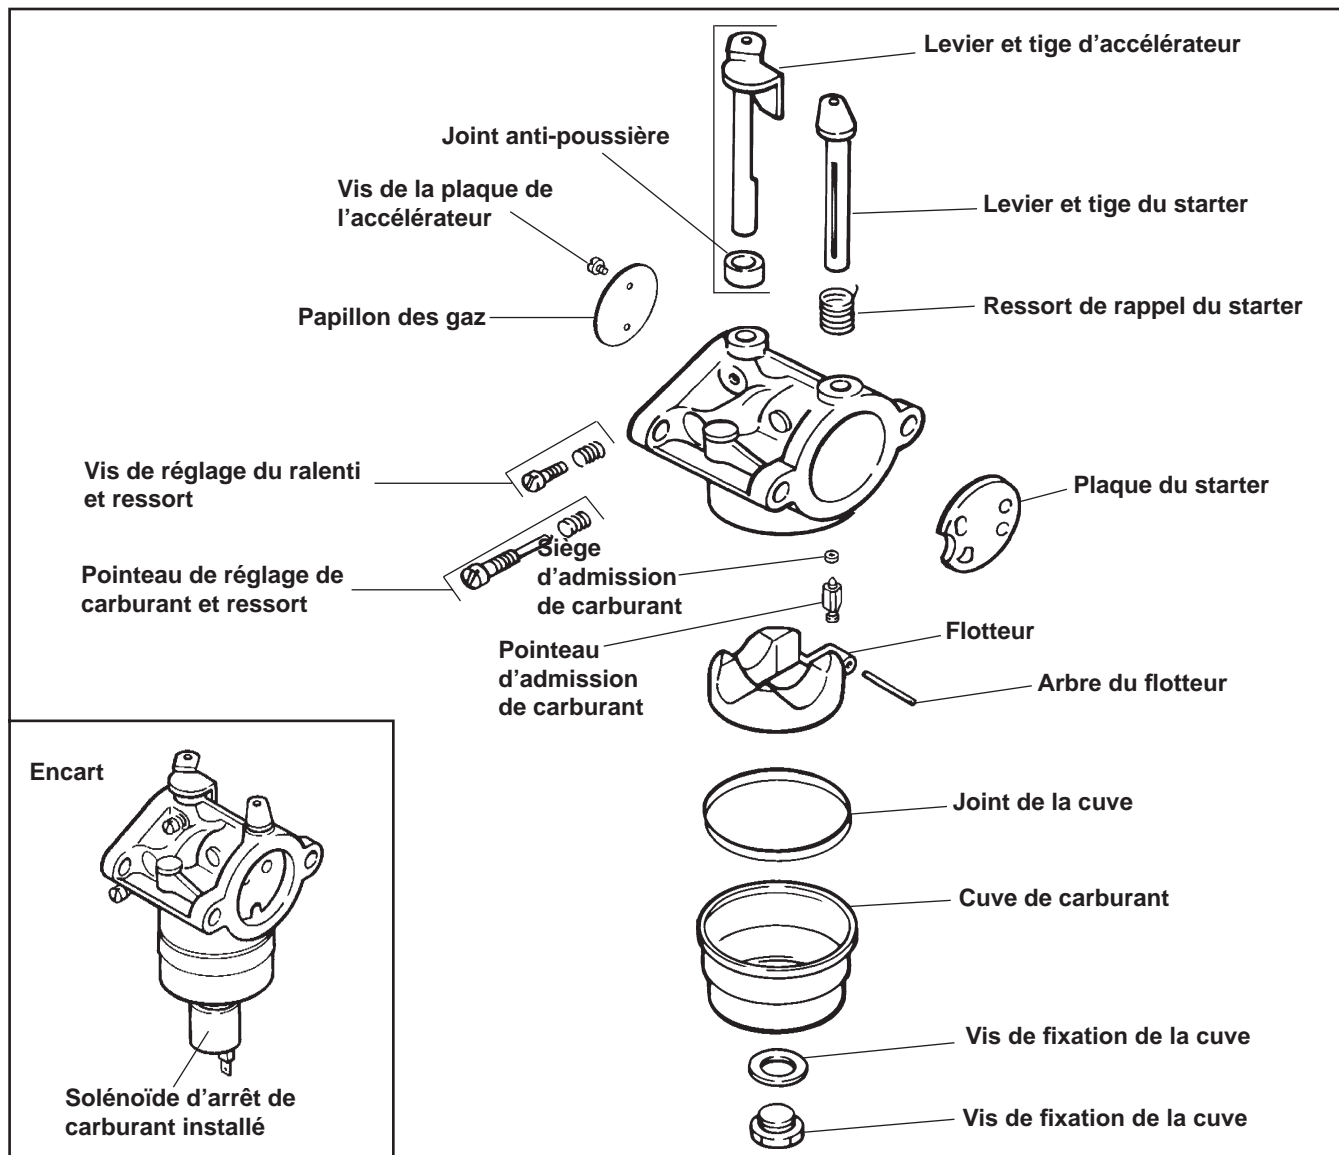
Carburateur réglable à gicleur principal - plan éclaté.
